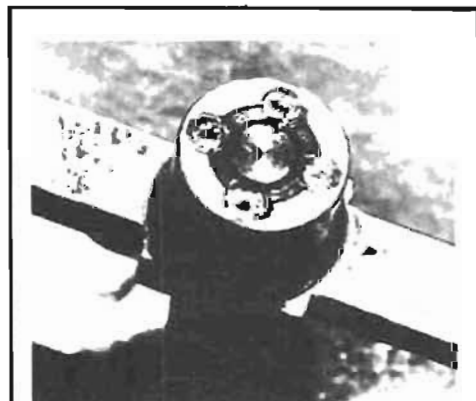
a. — Soudure par 4 points sur servo-valve équilibrée.
